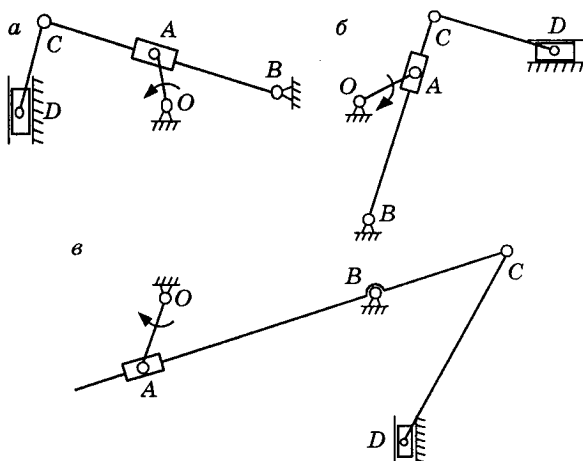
Схемы шестизвенных механизмов, используемых в технологическом оборудовании для обработки металлов давлением: а — горячая штамповка, гибка, прессование, брикетирование, б — чеканка, строгание, долбление, в — вырубка
